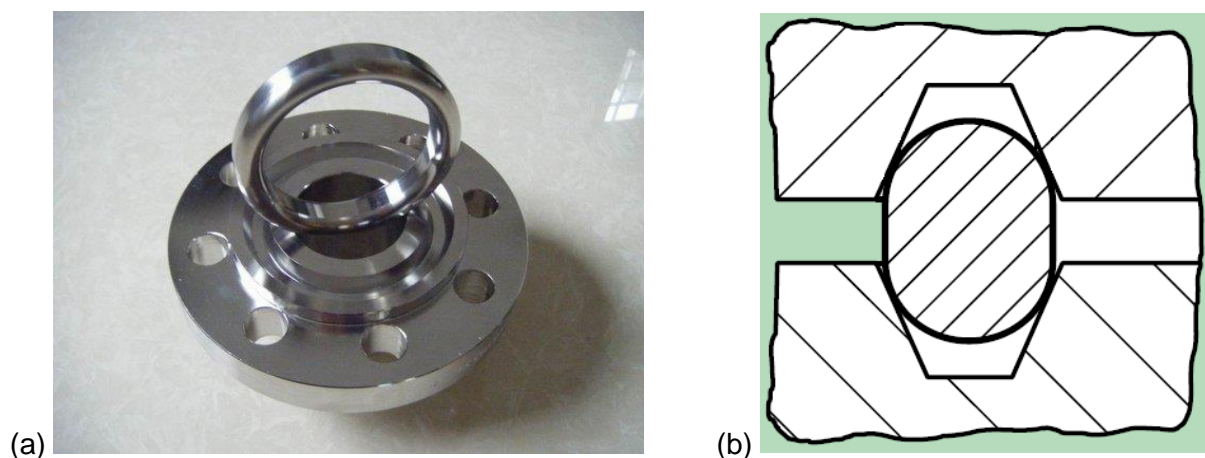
(a) Flange e anel de vedação e (b) ilustração da seção transversal de um anel e o canal de um flange. Adaptado de [3].
